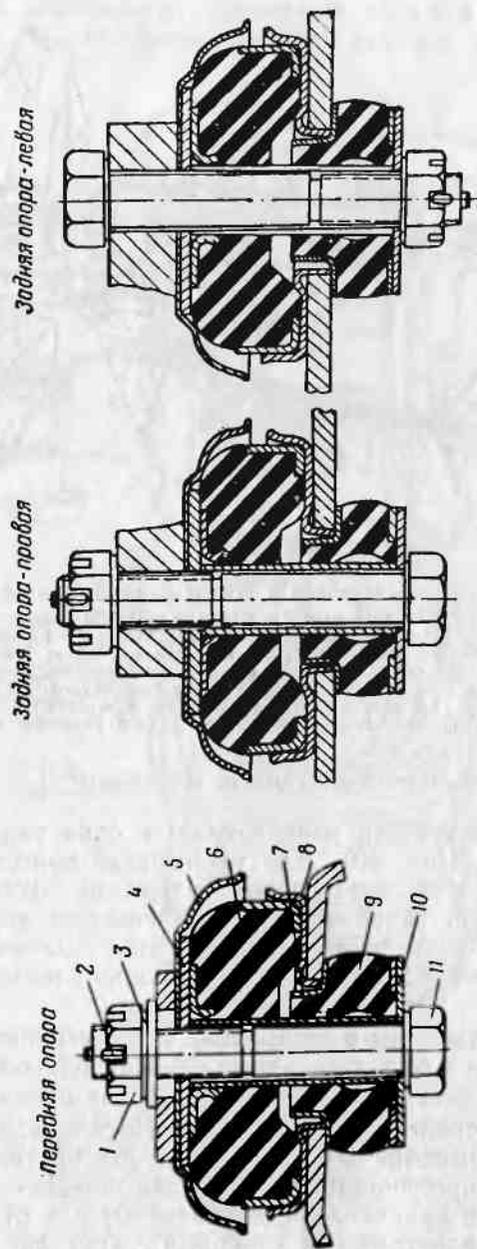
Установка резиновых подушек в опорах крепления двигателя (обозначения те же, что и на рис. 38)
